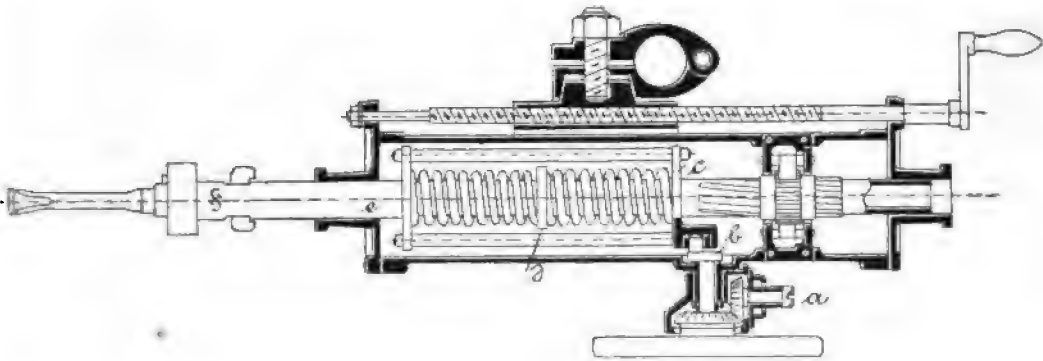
Siemens elektrische Stoßbohrmaschine.
